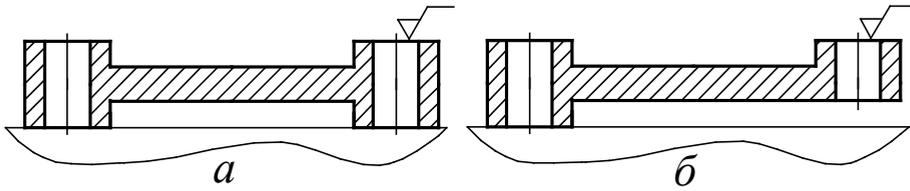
Конструкция деталей с опорными поверхностями:
